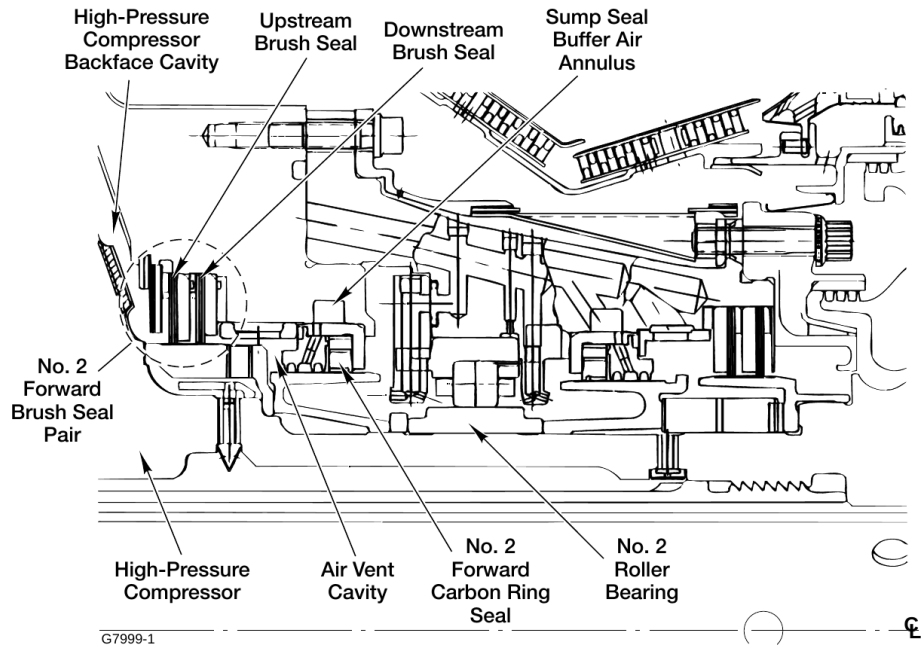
Компоновка щётчного уплотнения в двигателе JTAGG II [89]
